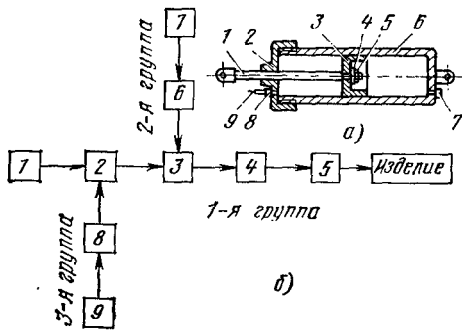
Силовой цилиндр и схема его сборки по базовой детали:
